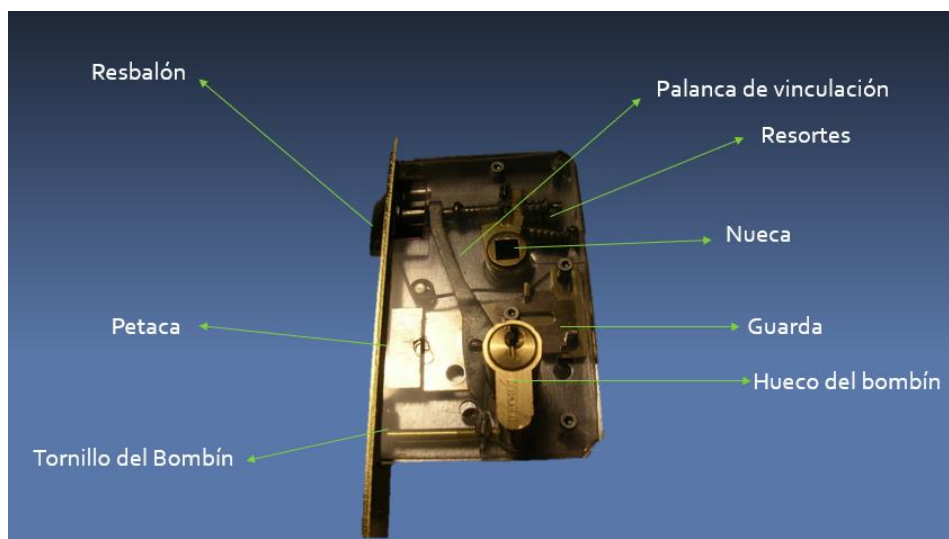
Partes de una cerradura de embutir. Fuente: CBCM
